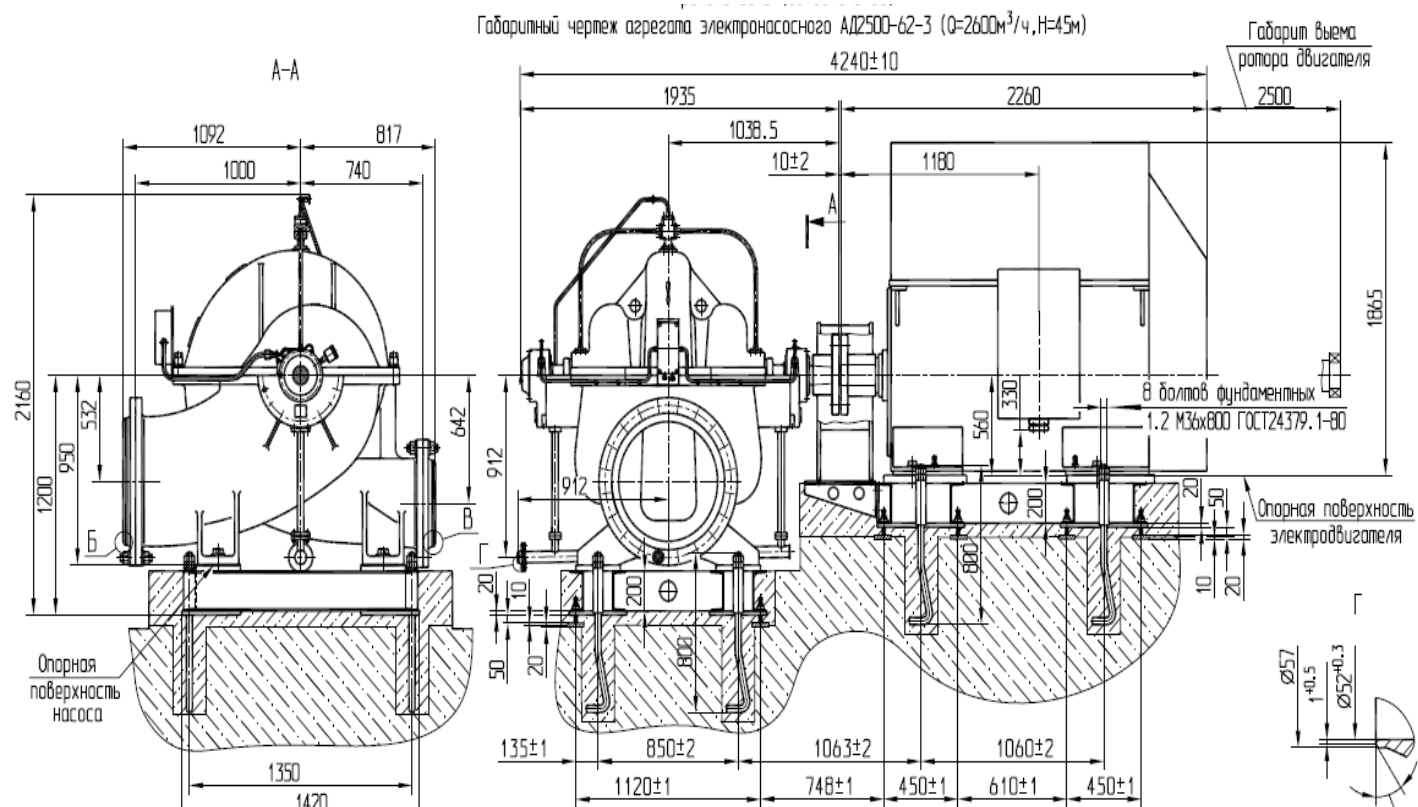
Габаритный чертеж насоса промконтура типа Д-2500-62-3
